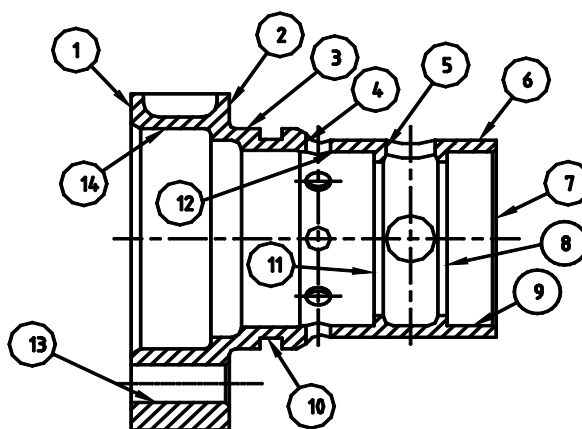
Схема розташування поверхонь деталі „Циліндрична втулка”
